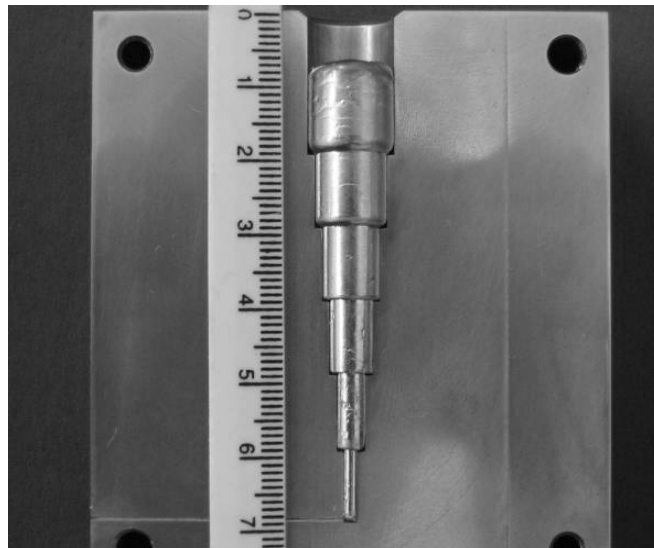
Amostra obtida por fundição em molde escalonado.
